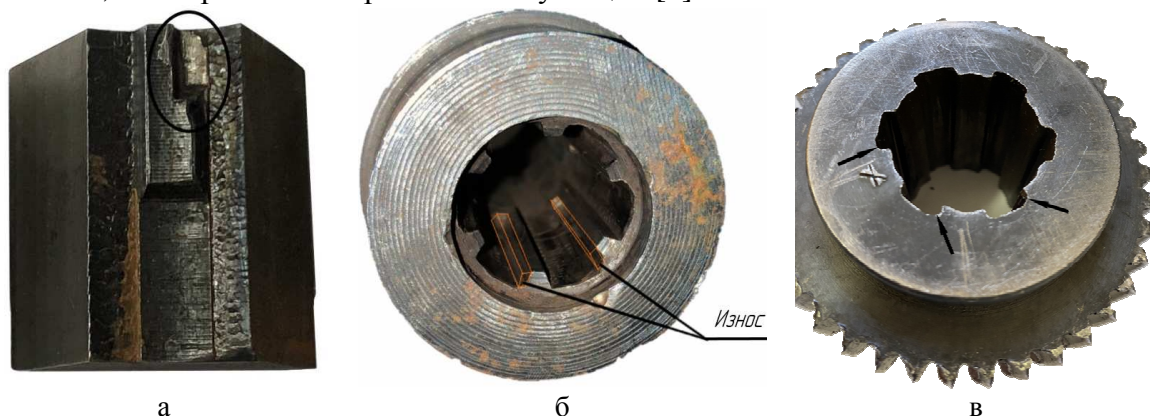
Износ боковых поверхностей шлицев втулок деталей: а – фрагмент муфты фланца ВМ 150.41.275-1, б - втулка привода насоса НШ-50А, в – зубчатое колесо привода токарно-винторезного станка 1ИС611В -1
